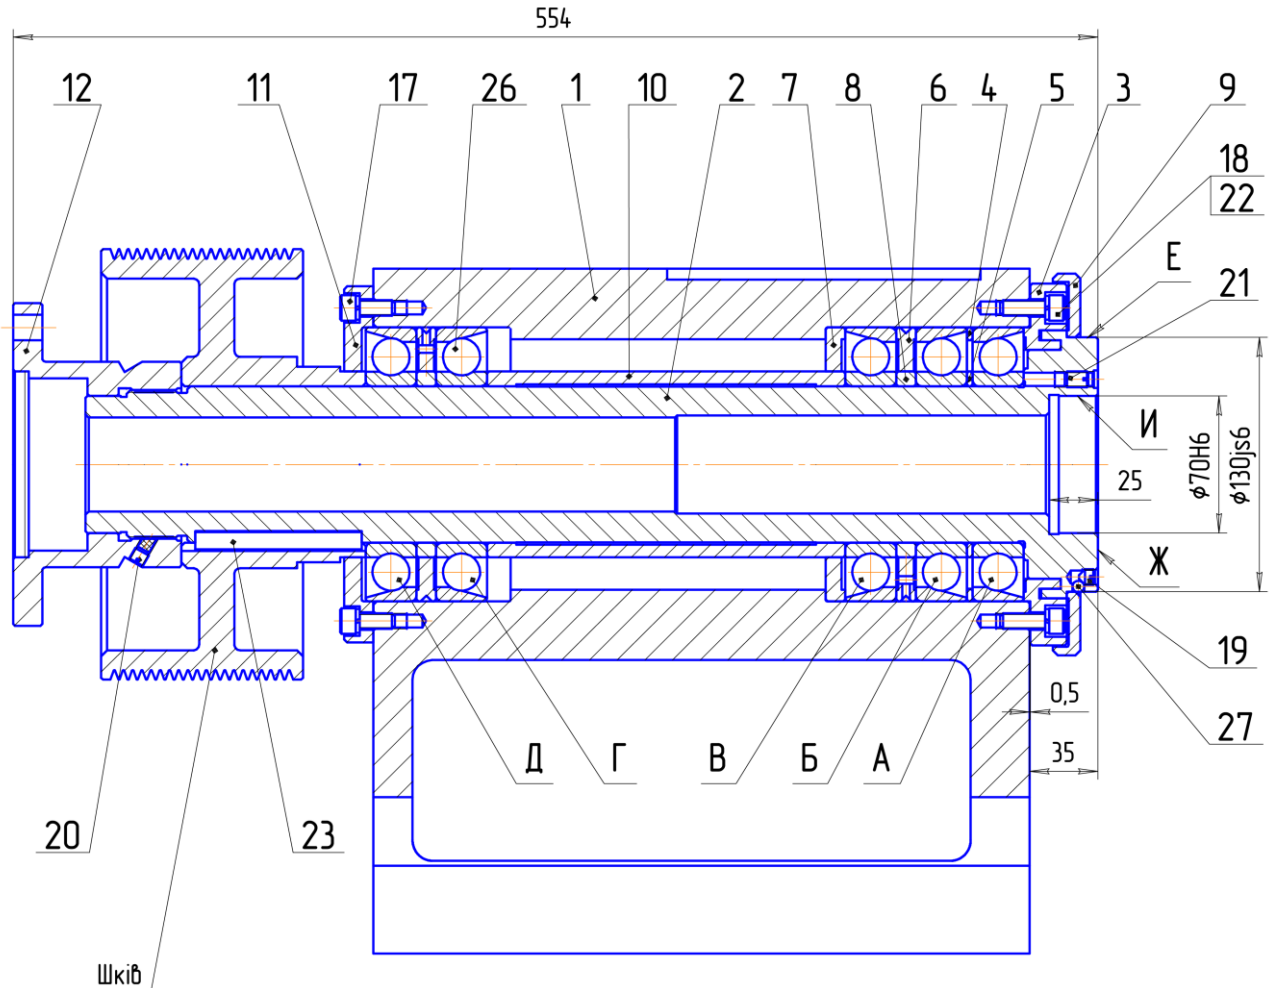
Шпиндельний вузол двошпиндельного токарного верстата з ЧПК мод. ПАБ-130
